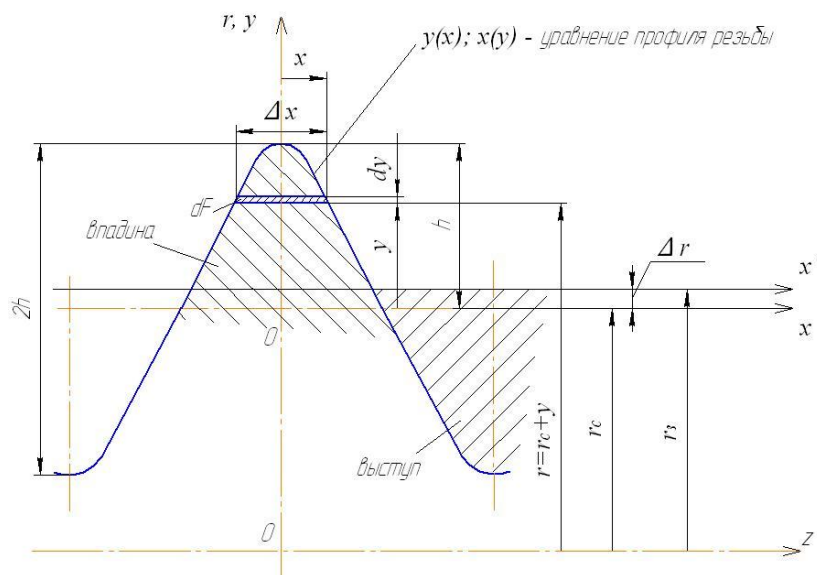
Модель профиля дюймовой резьбы для расчета диаметра под обработку накатыванием
